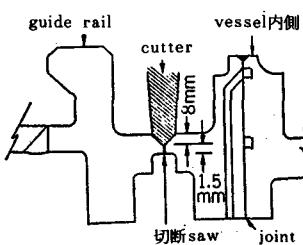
remote cutter와 真空vessel joint部의 車輪이 vessel내측의 guide rail 위를 走行한다. cutter는 용접시의 開先加工에도 사용된다. 本機는 実物크기 vessel(둘레 약 7m)의 mock-up시험에서 3시간에 1sector를 切断하고 있다. 그림 5에 vessel의 joint부 구조와 절단의 상황을 표시하였다.
